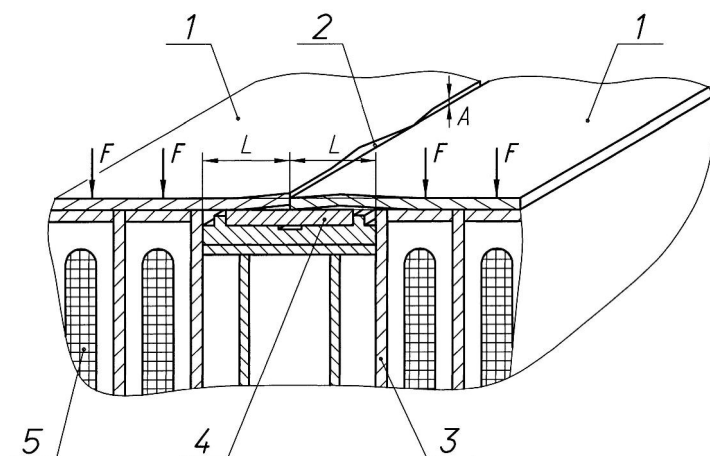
Схема сборки сварного стыка листового полотнища на электромагнитном стенде с медными подкладками
